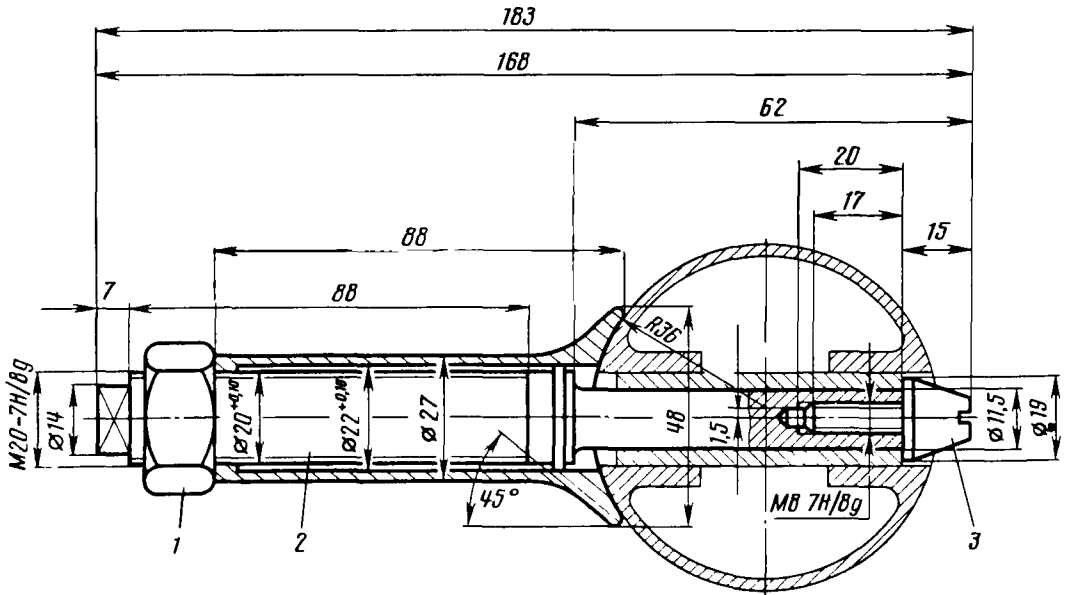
Приспособление для выпрессовки поршневого пальца:
